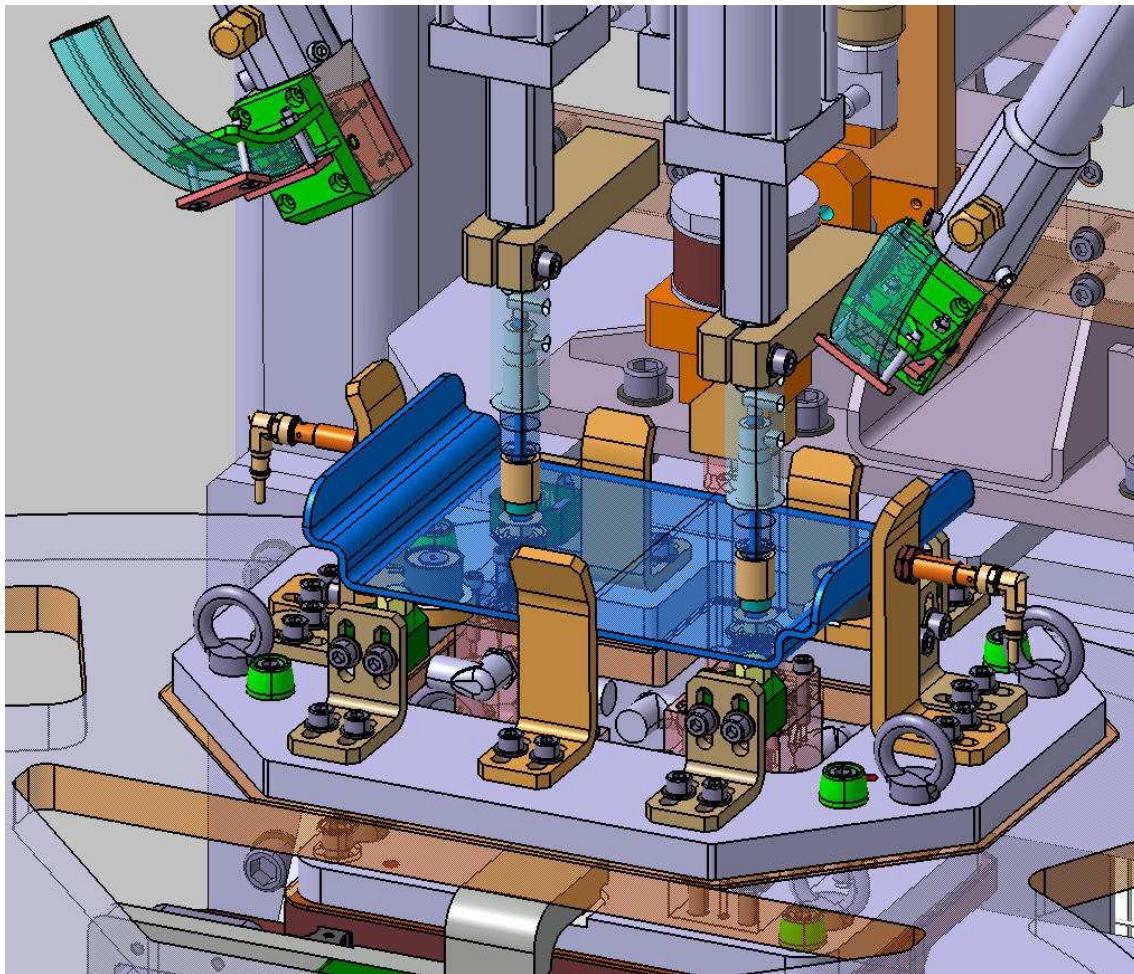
Electrodos en posición de soldadura.
